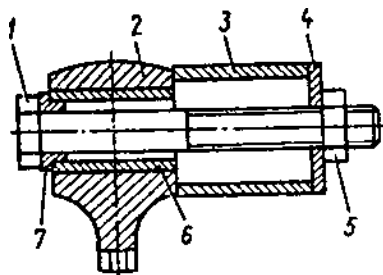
Выпрессовка втулки верхней головки шатуна с помощью приспособления:
